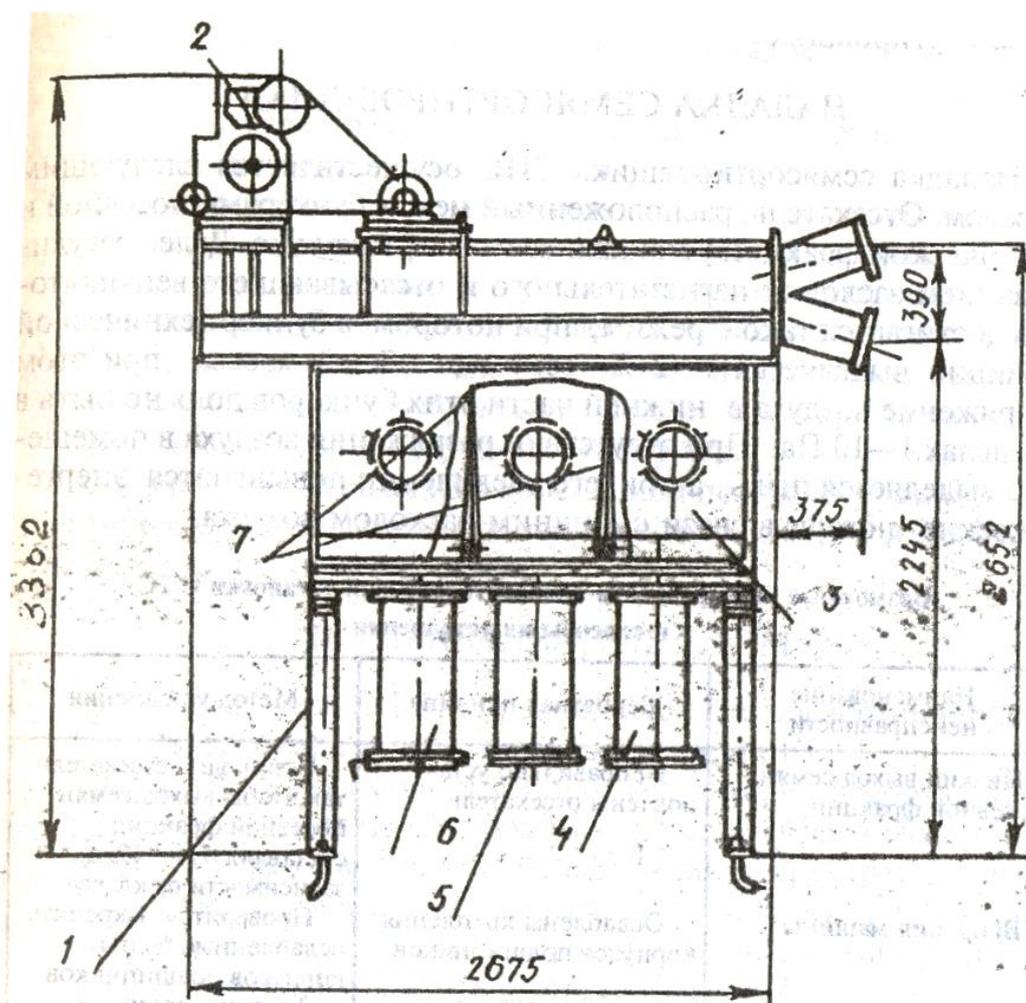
Устройство пневматической сеясортировочной установки СПС:
